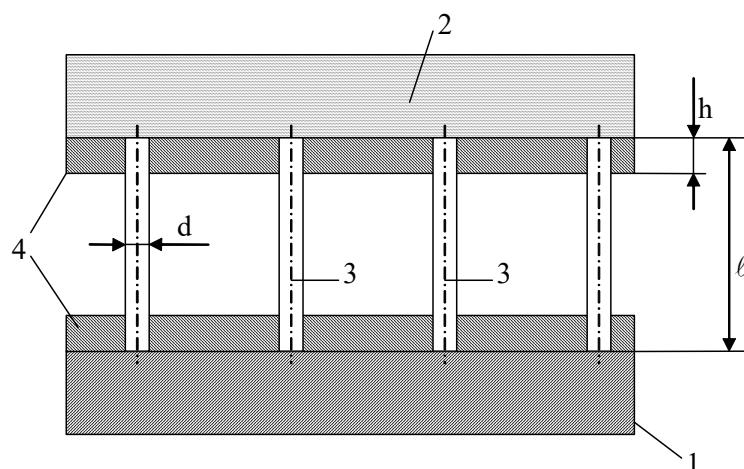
Схема паяного з'єднання: 1 – метал; 2 – кераміка;
